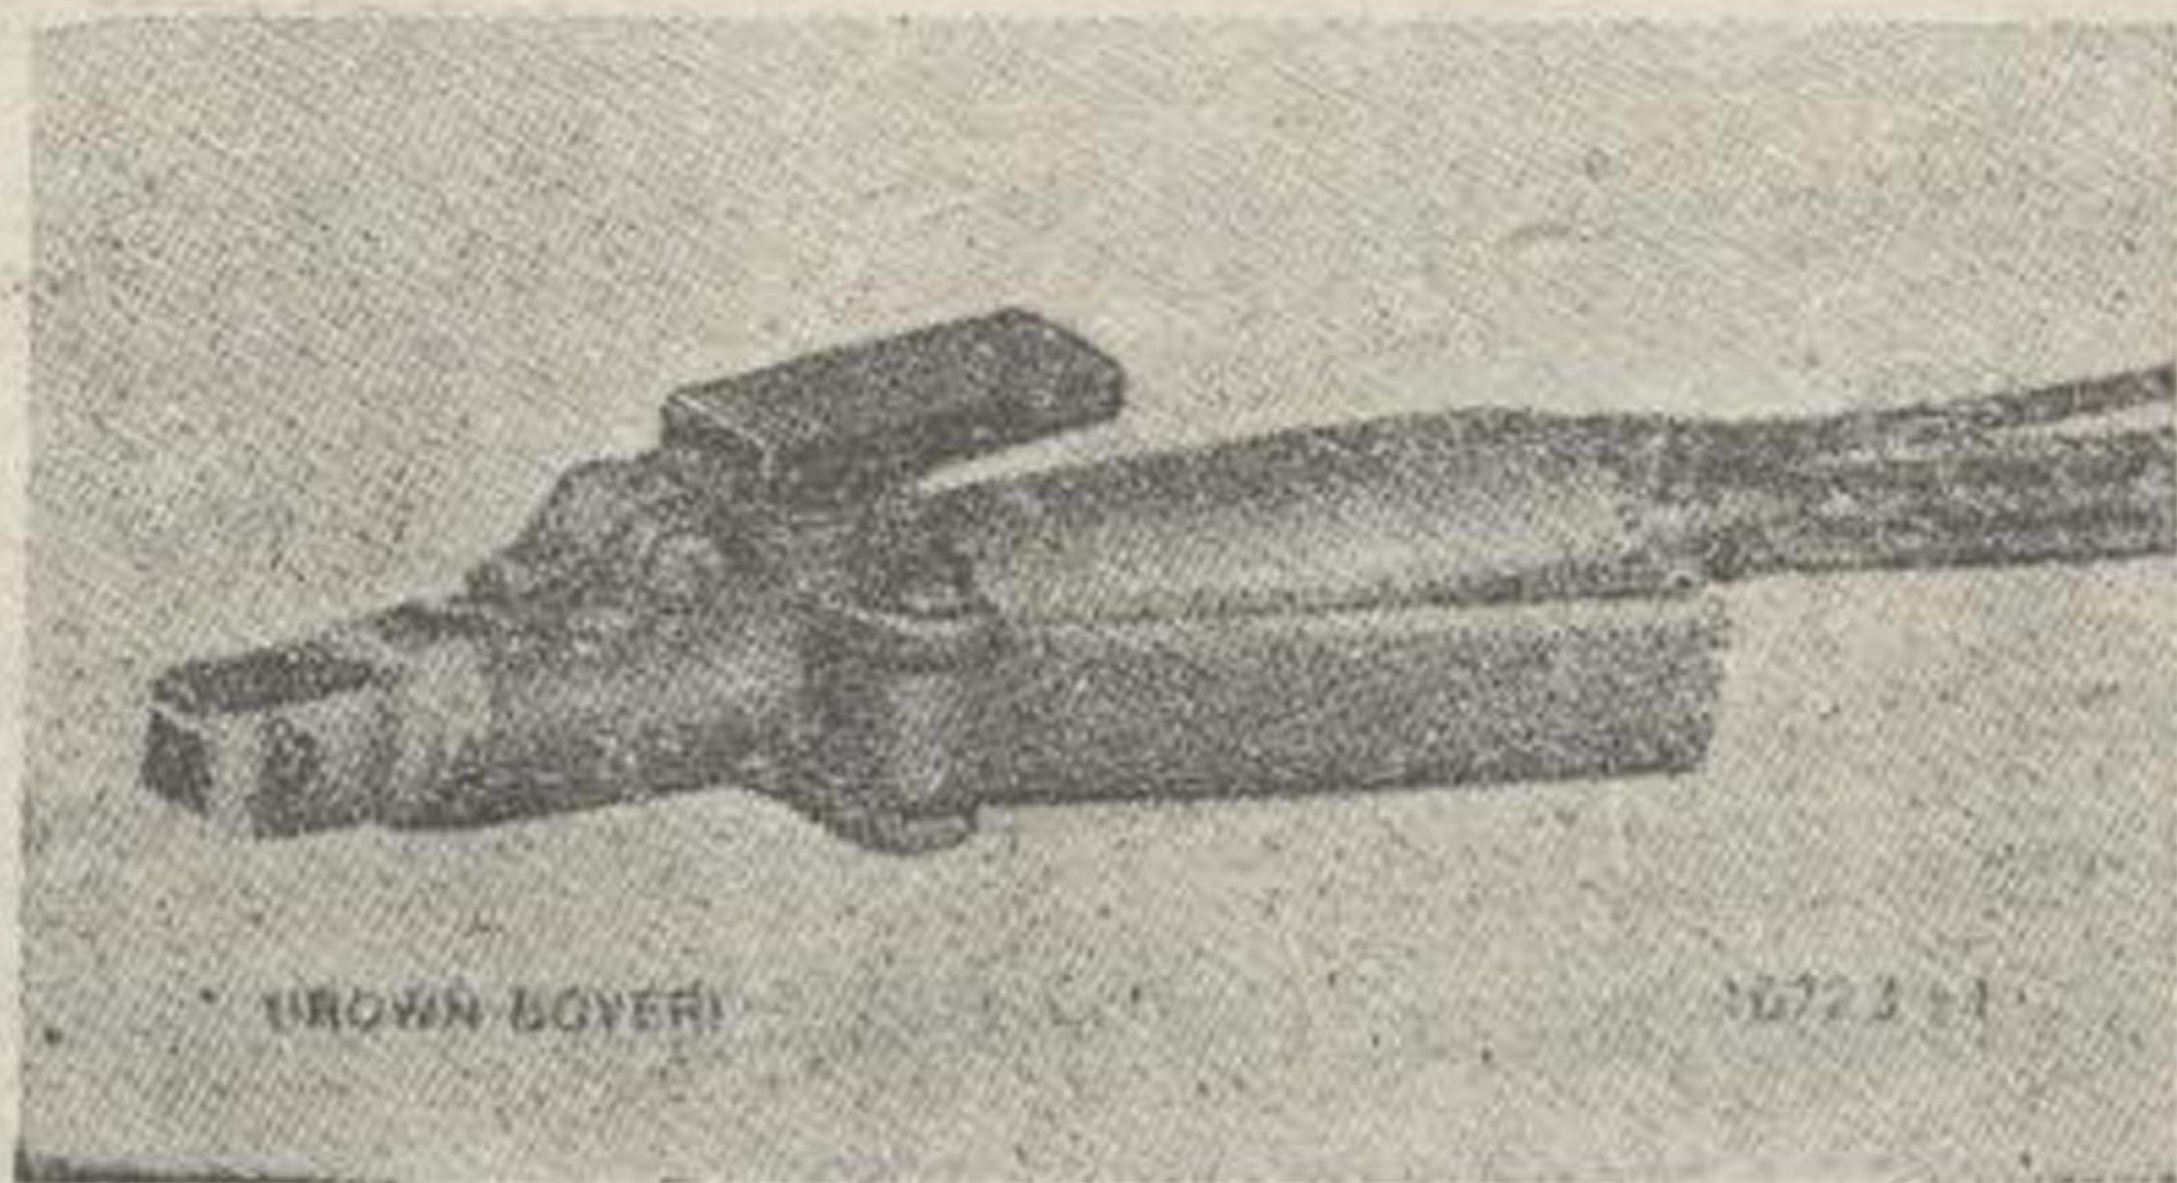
a — Pinza de soldar, construcción Brown Boveri.
